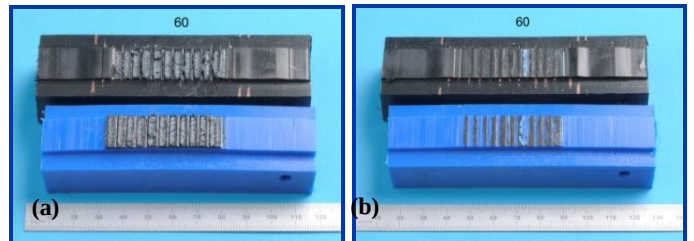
SUPERFICIES DE FRACTURA DE LAS PROBETAS EN UN ENSAYO DE PELADO DE SOLDADURAS POR EF EN TUBERÍAS DE 225 MM CON (A) FRACTURA DÚCTIL A LO LARGO DEL PLANO DE LOS ALAMBRES DE CALEFACCIÓN, Y (B) FRACTURA FRÁGIL EN LA INTERFAZ DE SOLDADURA
